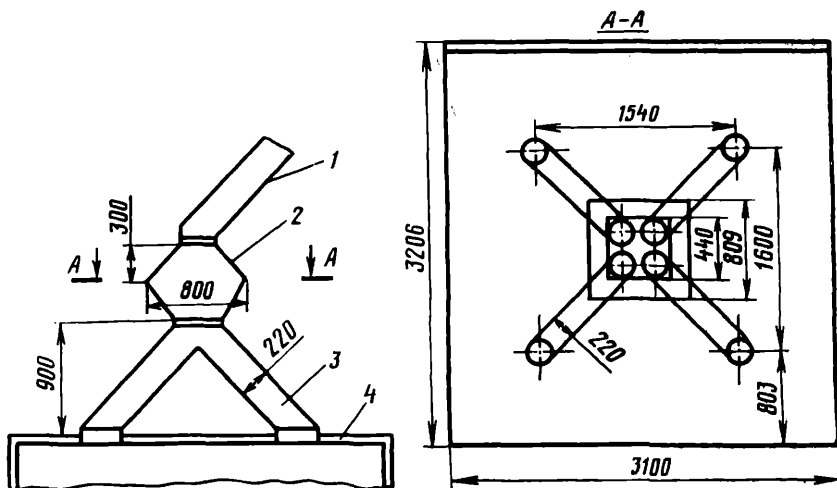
Устройство для загрузки шахтной зерносушилки:
